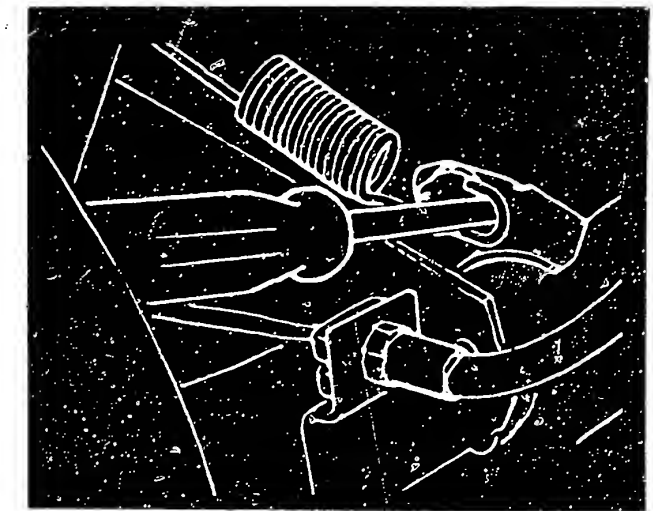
Vorspannen der Rückzugfeder des Bremskraftreglers mit einem 6,0mm dicken Schraubenzieher für die Grundeinstellung der Hinterradbremse.
